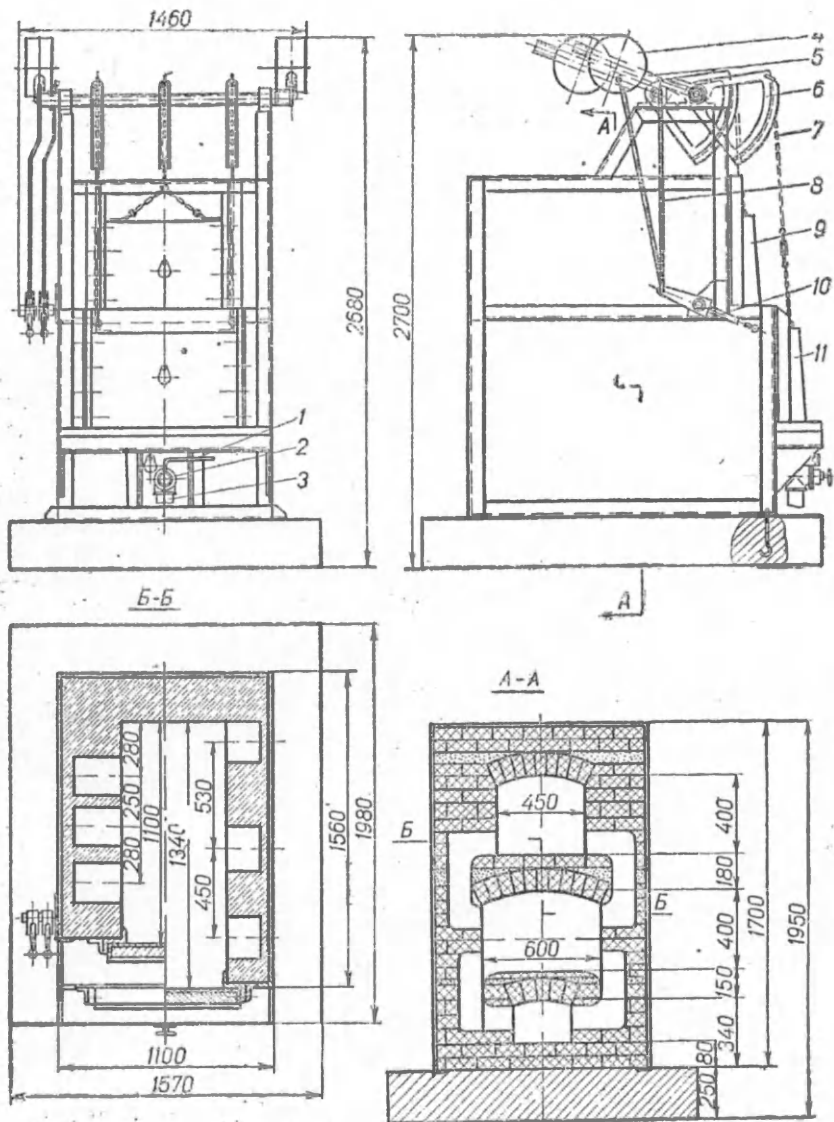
Печь пламенная двухкамерная с вертикально расположенными камерами для нагрева головок под сварку (общий вид):
